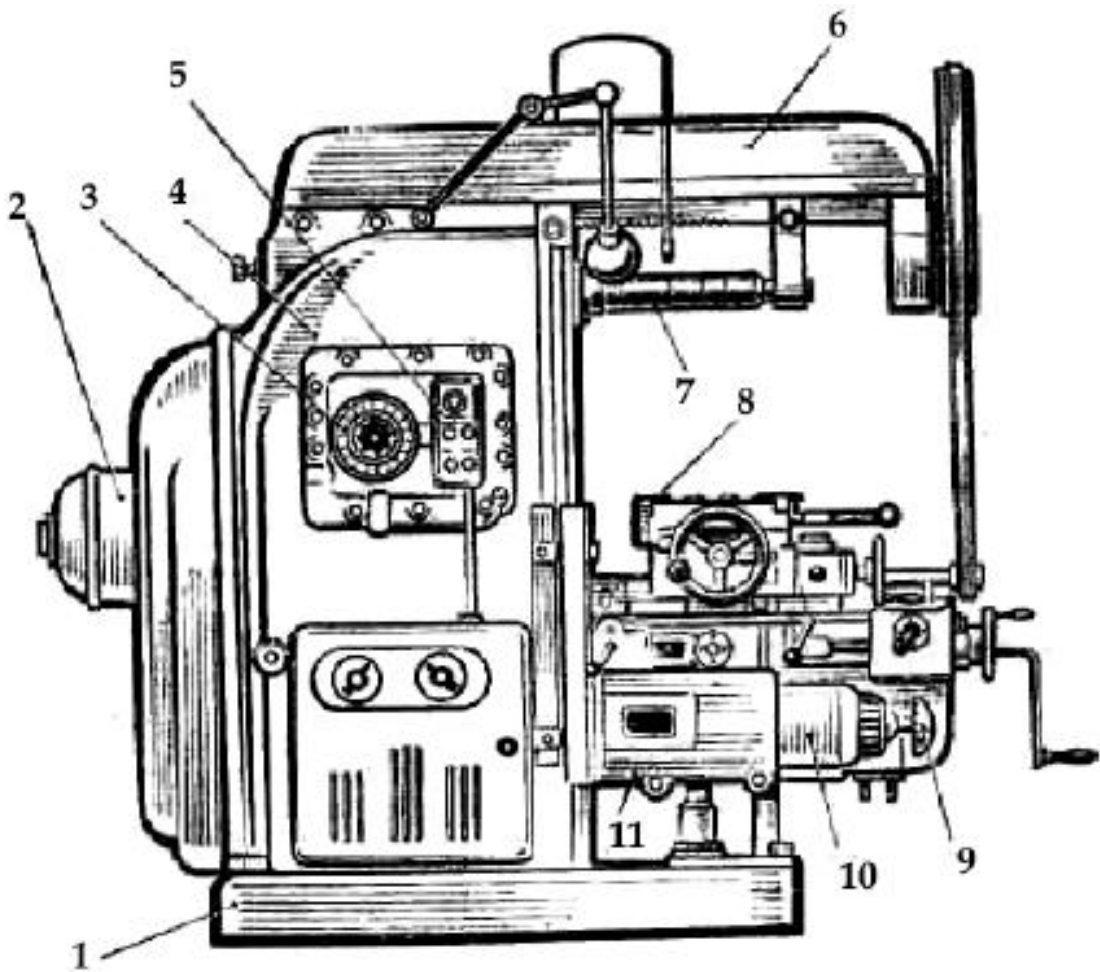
Основні елементи горизонтально-фрезерного станка моделі 6М82Г: 1 – основа; 2 – електродвигун приводу шпинделя; 3 – коробка
